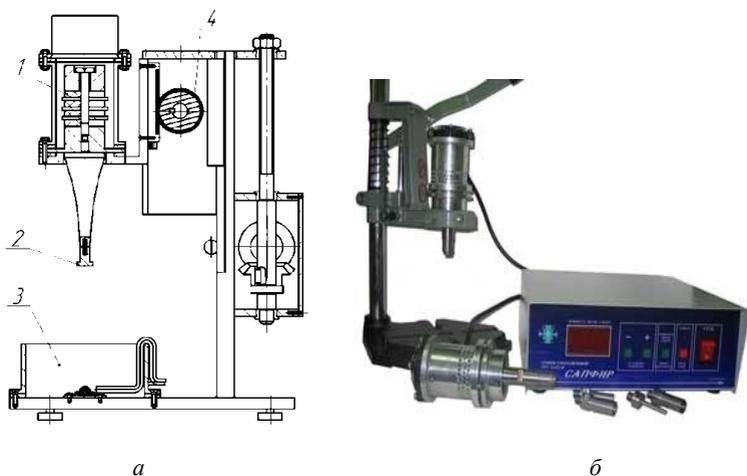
Схема устройства (а) и общий вид (б) ультразвукового станка для прошивания отверстий
